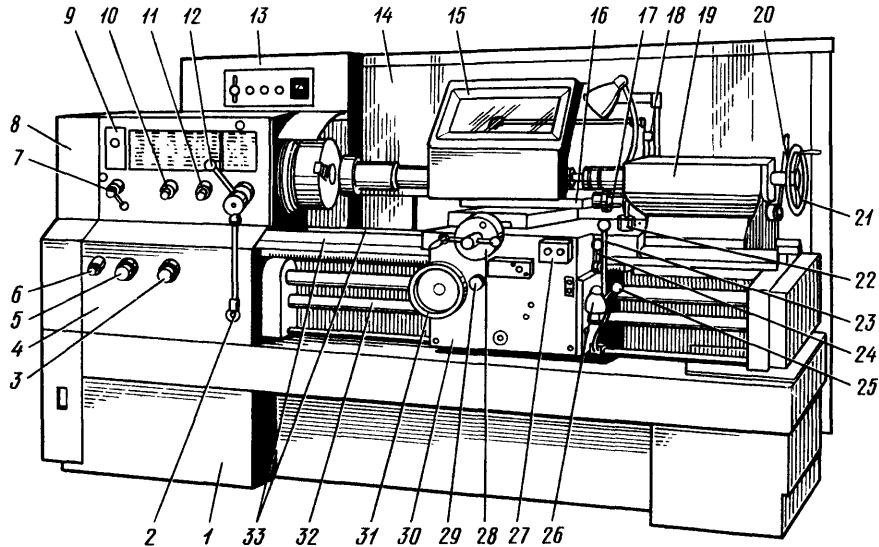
Общий вид и размещение органов управления токарно-винторезного станка модели 16К20:
